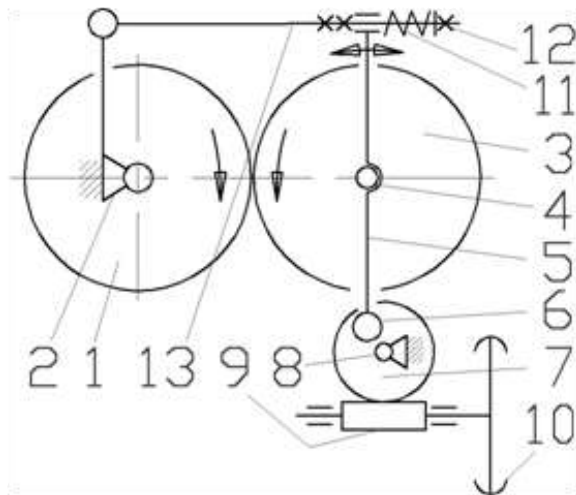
Схема установочного механізму плющильного станка.
